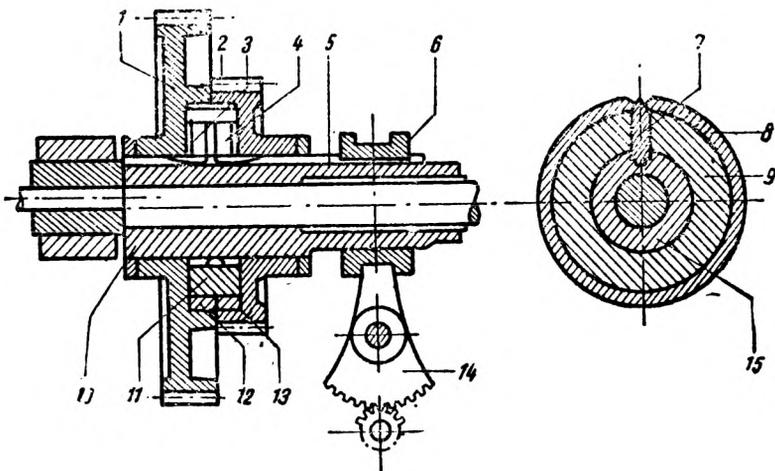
Передняя бабка токарного станка с двойным перебором (вид сзади)
